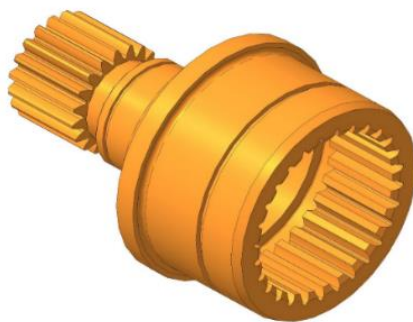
Твердотельная модель детали «Вал-шестерня»
